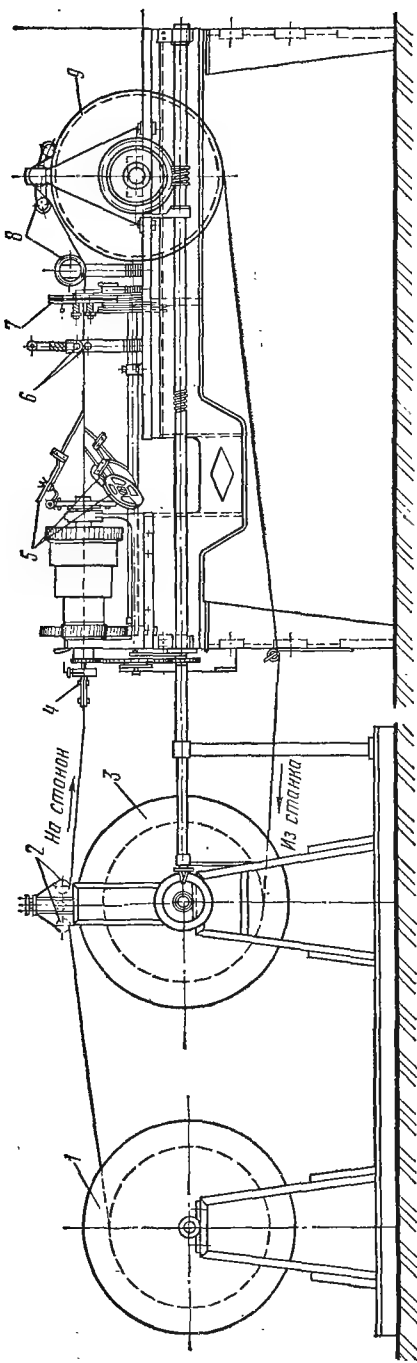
Токарный станок, приспособленный для изоляции обмоточных проводов (оплеточный станок):
